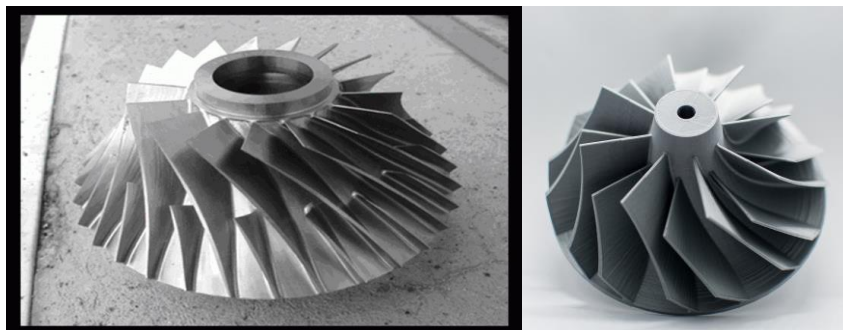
A la izquierda: turbina realizada en un centro de mecanizado de 5 ejes. Imagen extraída de: (34) A la derecha: turbina realizada mediante tecnología ALM. Imagen extraída de: (30)
